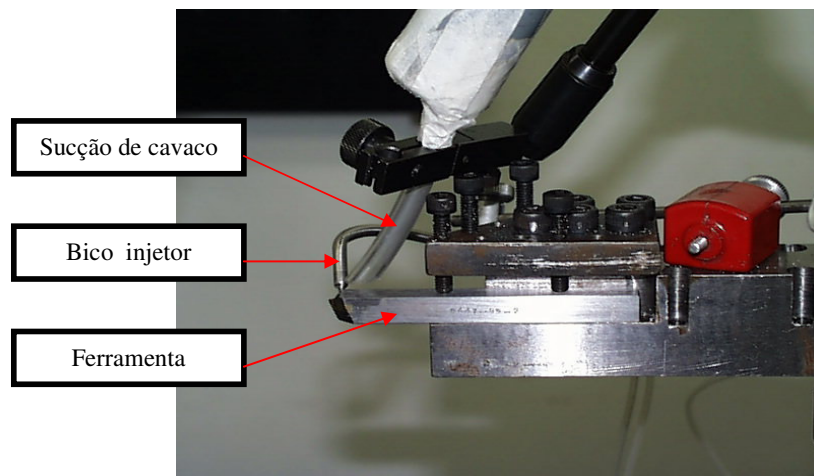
Bico injetor junto à ferramenta de corte.
